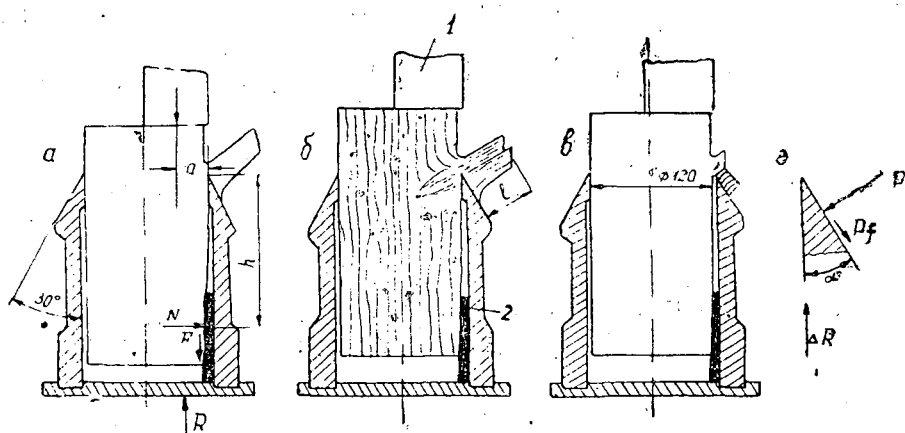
Обрезка сучьев цилиндрическими резцами.
